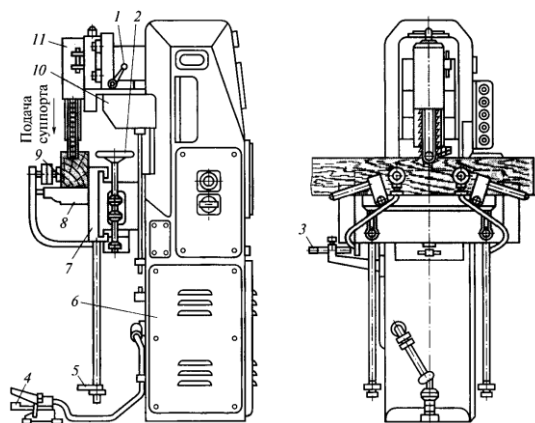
Ланцюгово-довбальний верстат: 1 – рукоятка; 2 – маховичок поздовжні подачі; 3 – обмежник ходу стола; 4 – педаль; 5 – упор; 6 – станина; 7 – вертикальна плита; 8 – горизонтальна плита; 9 – гідропритиск; 10 – супорт; 11 – ріжуча головка
